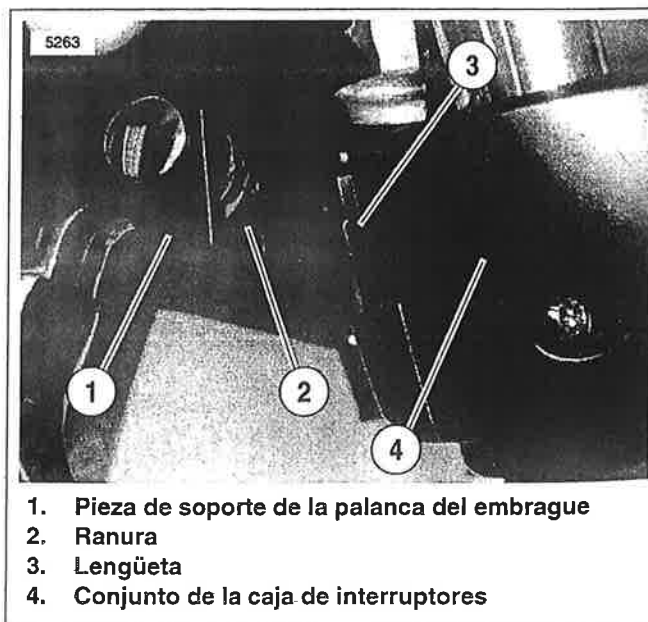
Ajuste de la pieza de soporte de la palanca de embrague en las cajas de interruptores del manillar izquierdo
